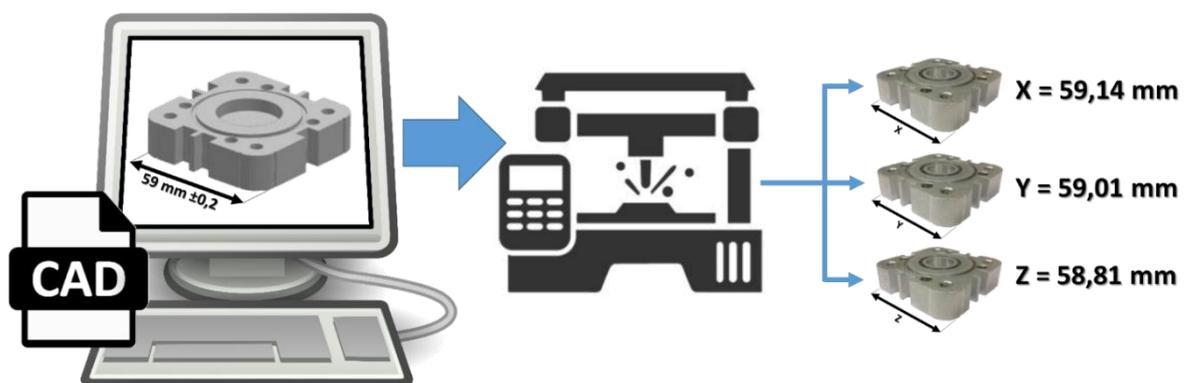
Dimensão real única de componentes, adaptado de Picard [4]
